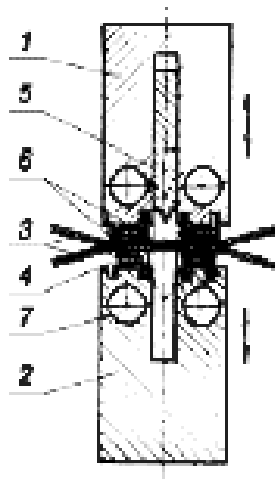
Губки зварки термоімпульсної. 1 – верхня губка; 2 – нижня губка; 3 – матеріал пакувальний; 4 – спіраль нагрівна; 5 – рухомий ніж; 6 – ізолюючі стрічки; 7 – охолоджуючі канали.
